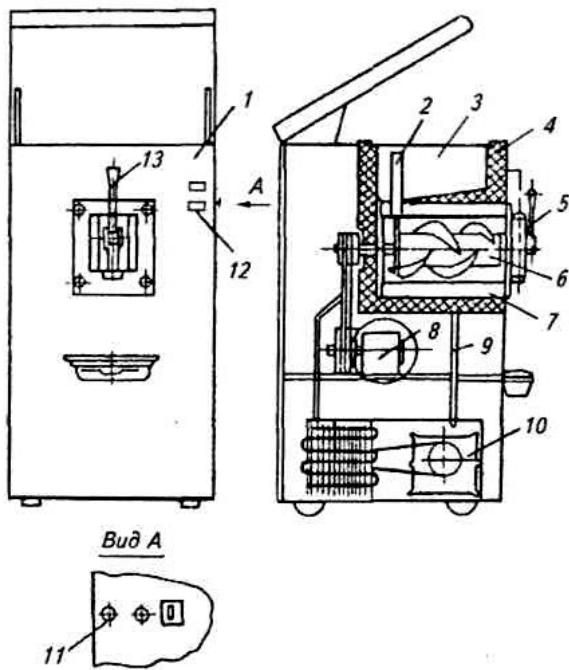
Фризер ФМ-1: 1 — корпус; 2— дозатор; 3 — бак; 4 — теплоизо-ляция; 5— отборное устройство; 6 — мешалка; 7—рабочий цилиндр; 8— привод мешалки; 9— трубопровод; 10— холодильный аппарат; 11 — терморегуля-тор; 12 — шкала; 13 — рукоятка
